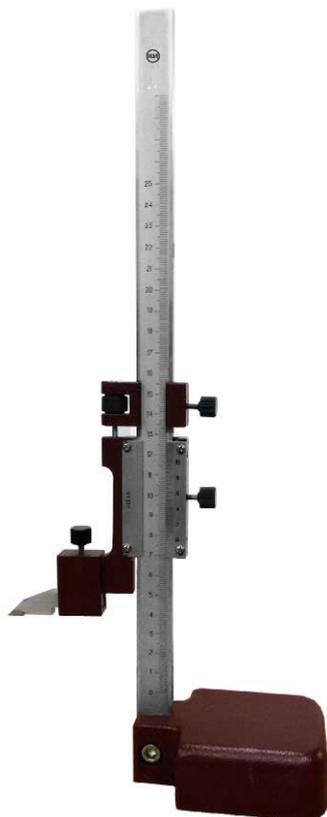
Общий вид штангенрейсмасов типа ШР
